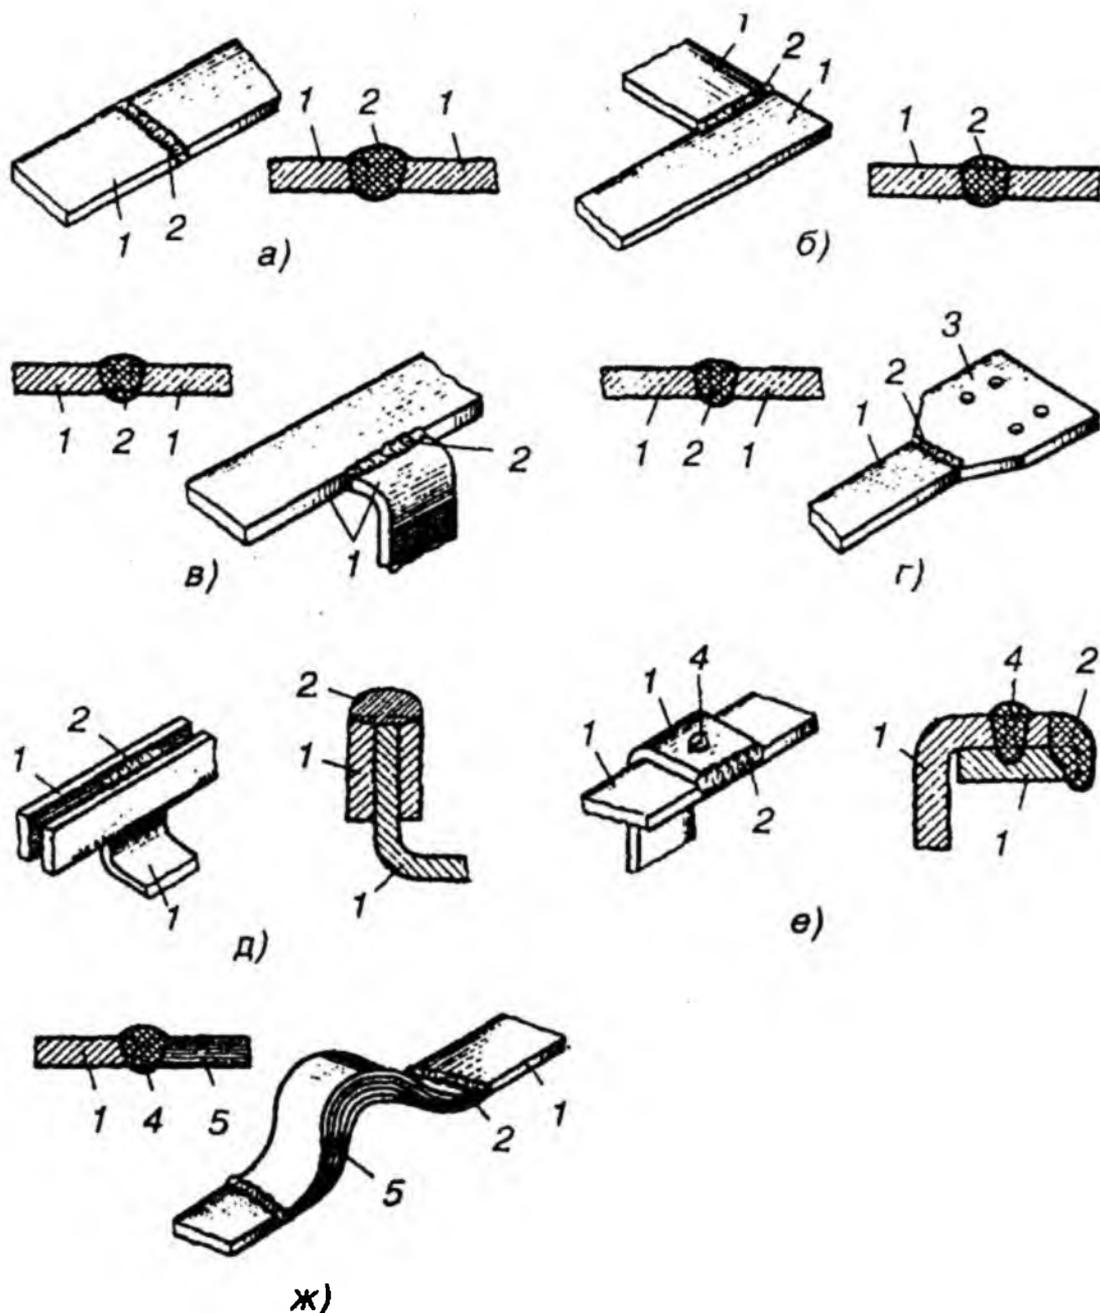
Варианты сварных соединений прямоугольных шин и ответвлений:
